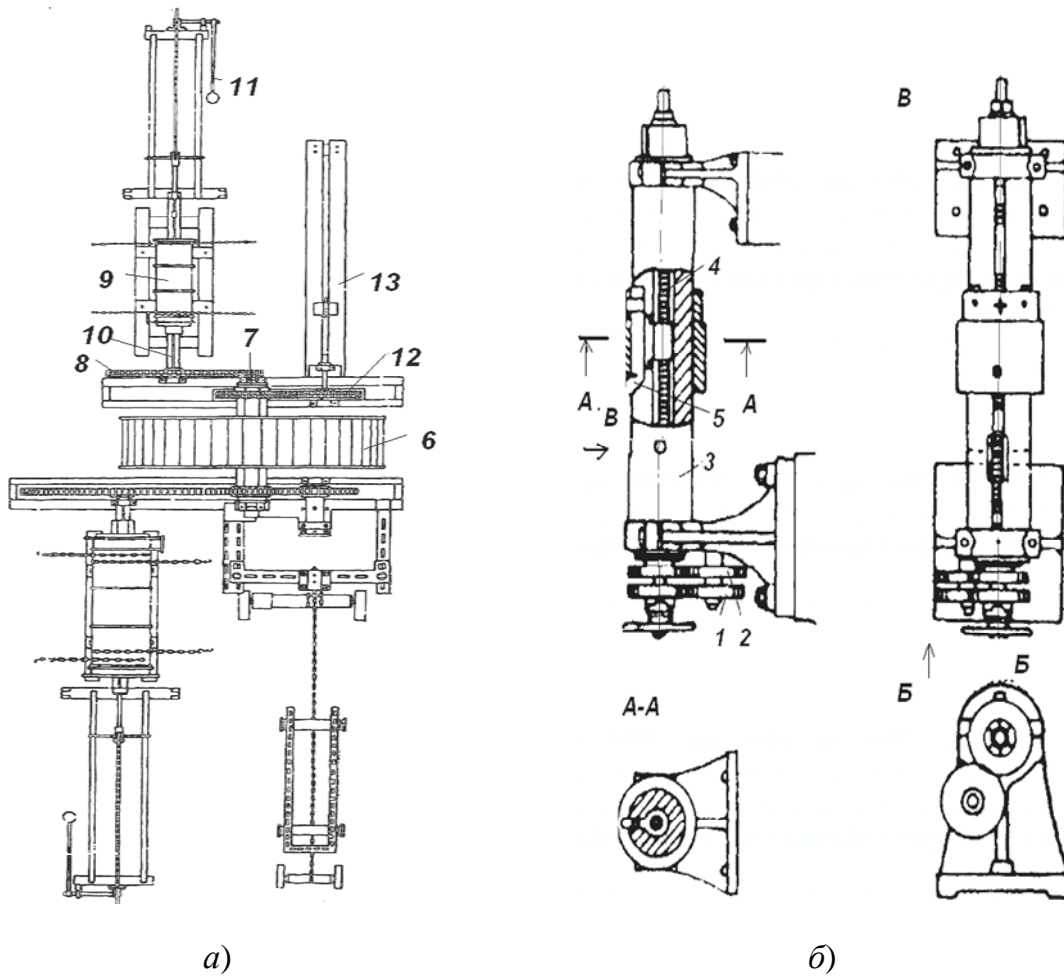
Чертеж станка Вилкинсона (а) и борштанги (б)
